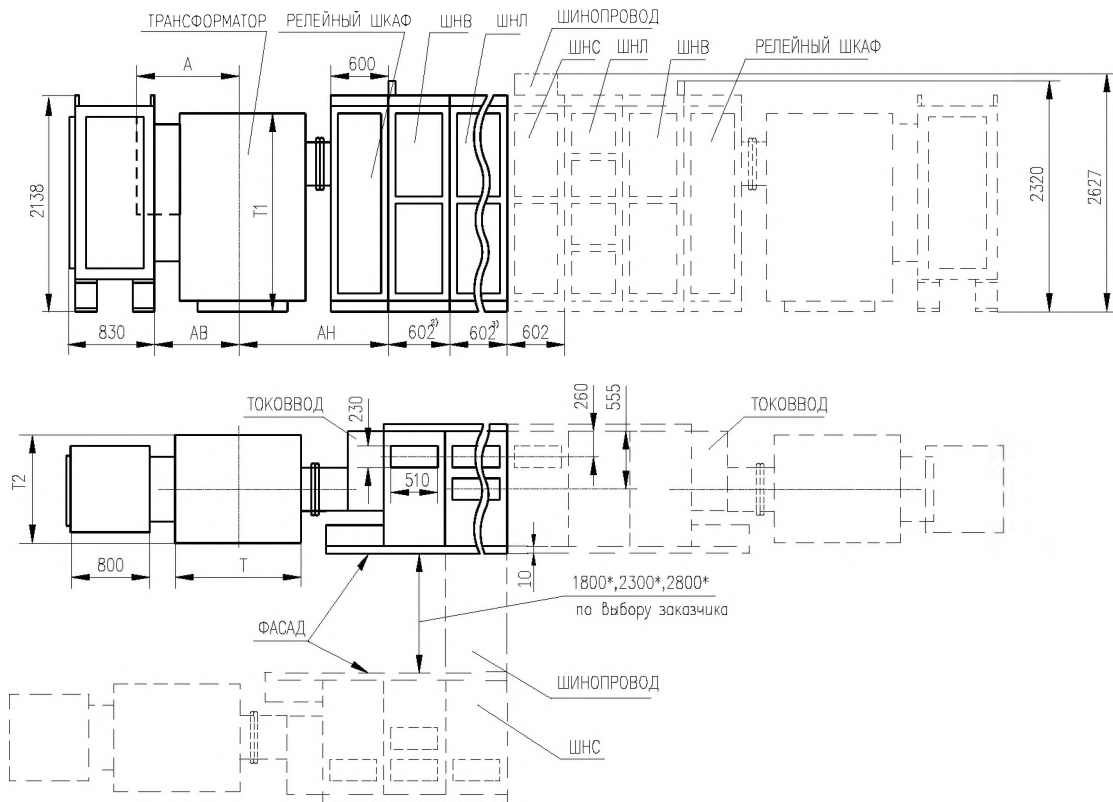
Габаритные размеры КТП 250...1000 с РУНН сборной конструкции со шкафом ШВВ-2Р или ВВ-1
